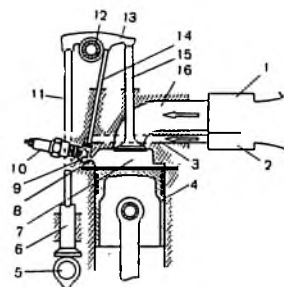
Схема двигателя с форкамерно-факельным зажиганием: 1 — карбюратор; 2 — форкамерная часть карбюратора; 3 — канал питания форкамеры; 4 — поршень; 5 — распределительный вал; 6 — толкатель; 7 — основная камера сгорания; 8 — сопловое отверстие; 9 — форкамера; 10 — свеча; 11 — штанга; 12 — ось коромысла; 13 — коромысло; 14 — форкамерный клапан; 15 — впускной клапан основной камеры; 16 — впускной канал.
